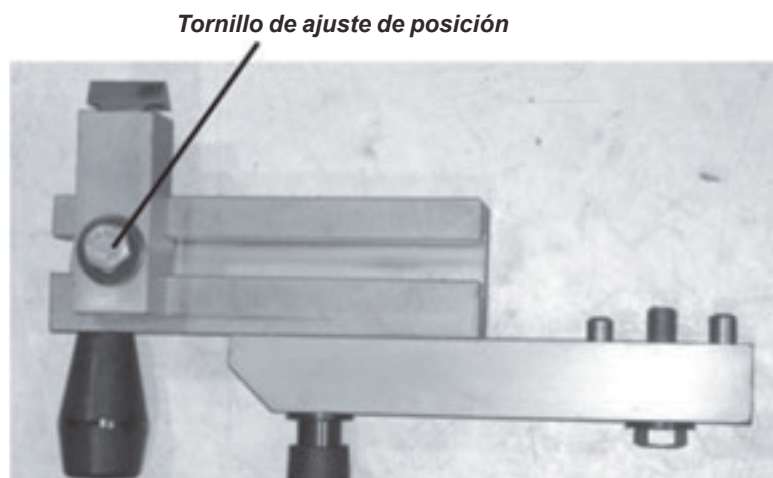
Afloje el tornillo de ajuste de posición para ajustar el desenganche radialmente.
